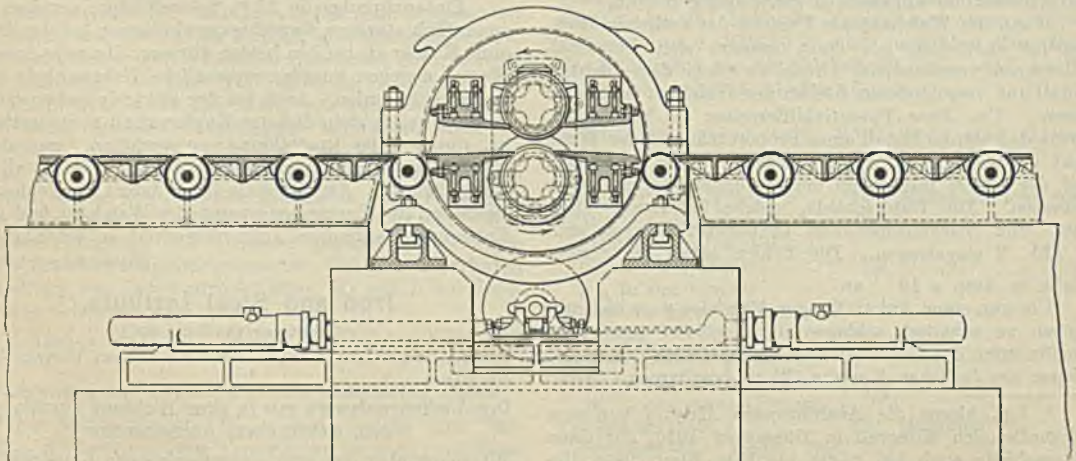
Umkehrduo mit durchlaufendem Antrieb. Wendevorrichtung des Walzgerüsts.
